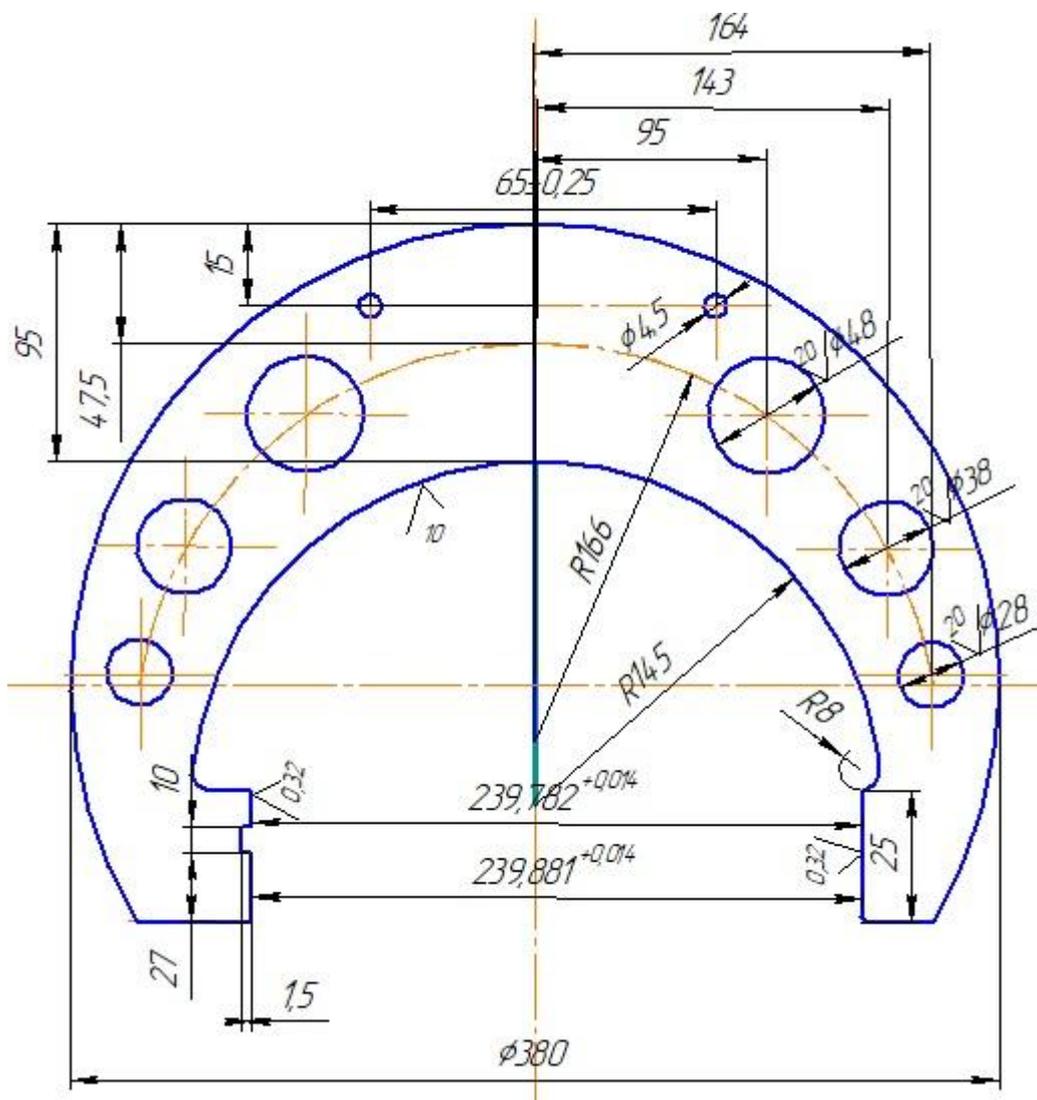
Ескіз скоби для контролю вала Ø 240e8
